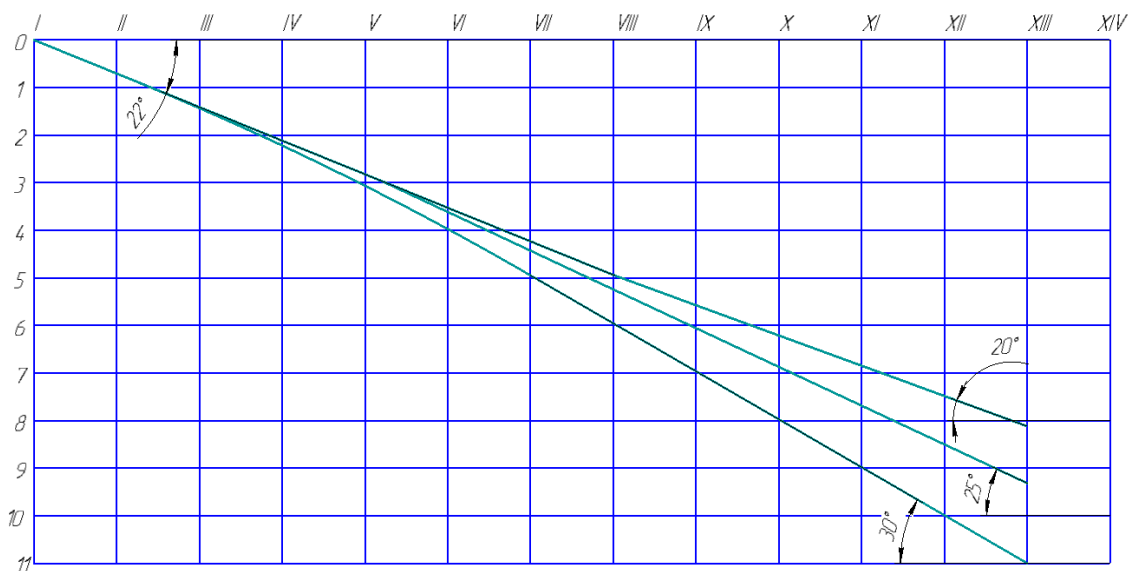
Профілювання поверхні лопаті на розгортці циліндра
